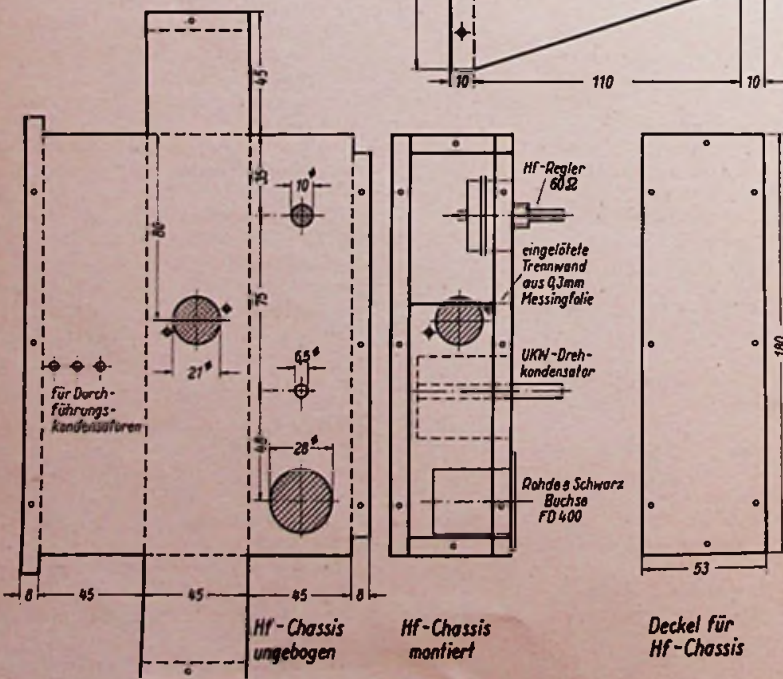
Teile für den Hf-Baustein. Werkstoff: Messingblech 1 mm
